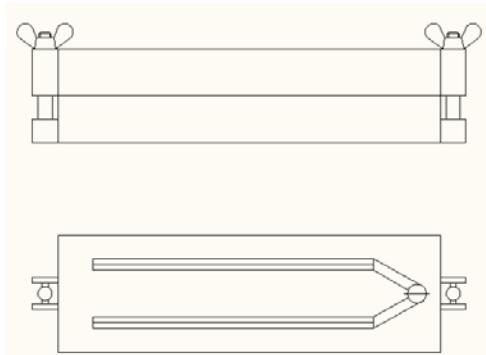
Пресс-форма для получения образцов для испытания на прочность
